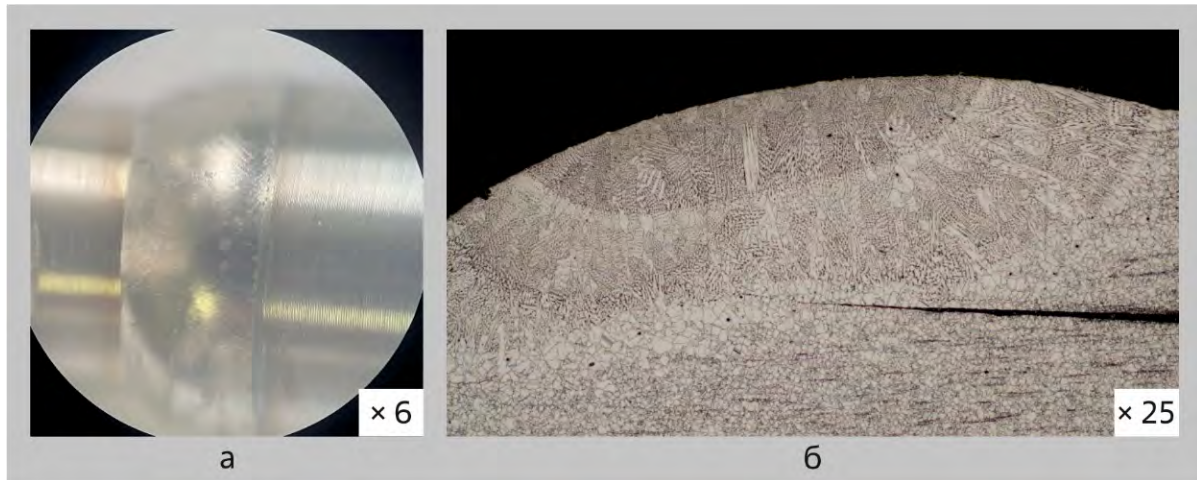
Внешний вид (а) и структура (б) торцового сварного соединения сплава NM20V3-VЧ
